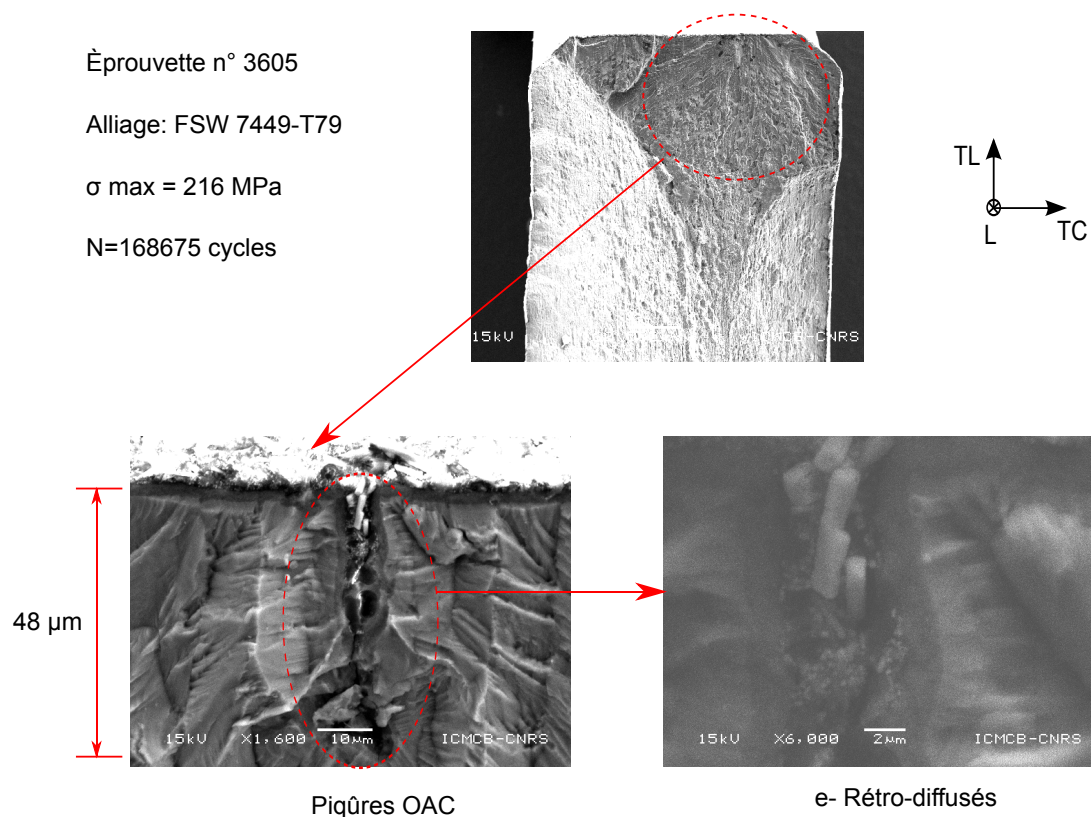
Fractographie d’un faciès de rupture d’une éprouvette T10 prélevée dans le sens L du joint soudé en alliage 7449-T79
